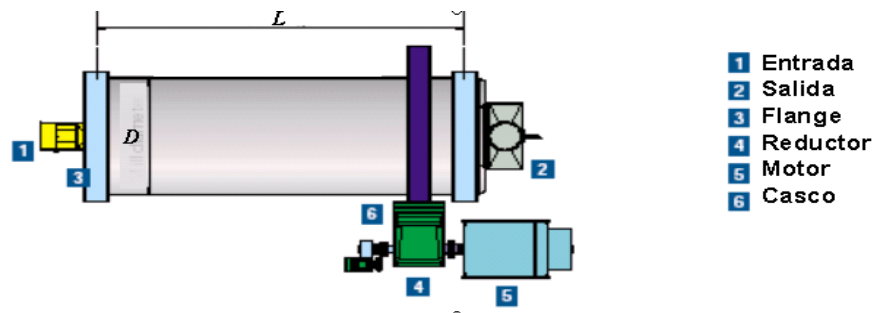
Vista exterior de un molino cilíndrico (Dimensionado de molinos, 2003)
